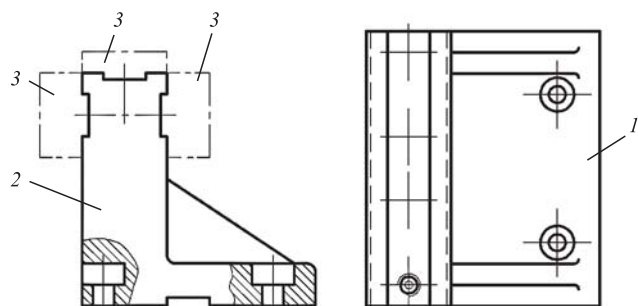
Перспективная конструкция корпуса линейной протяжки
